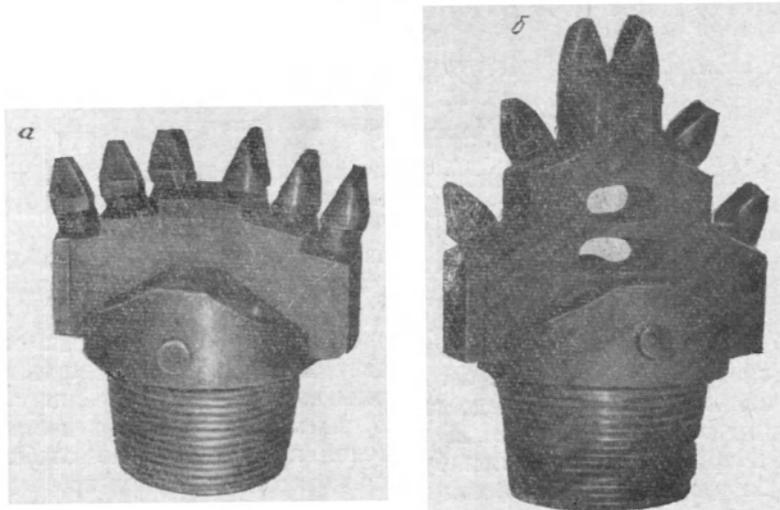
Буровые коронки для станка БСШ-1м конструкции авторов:
